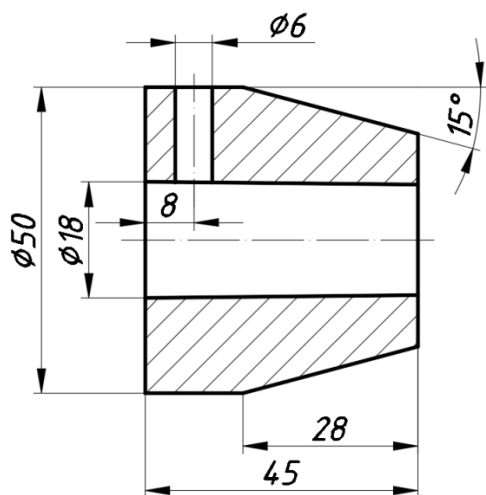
Образец выполнения чертежа детали, частично ограниченной конической поверхностью вращения.
